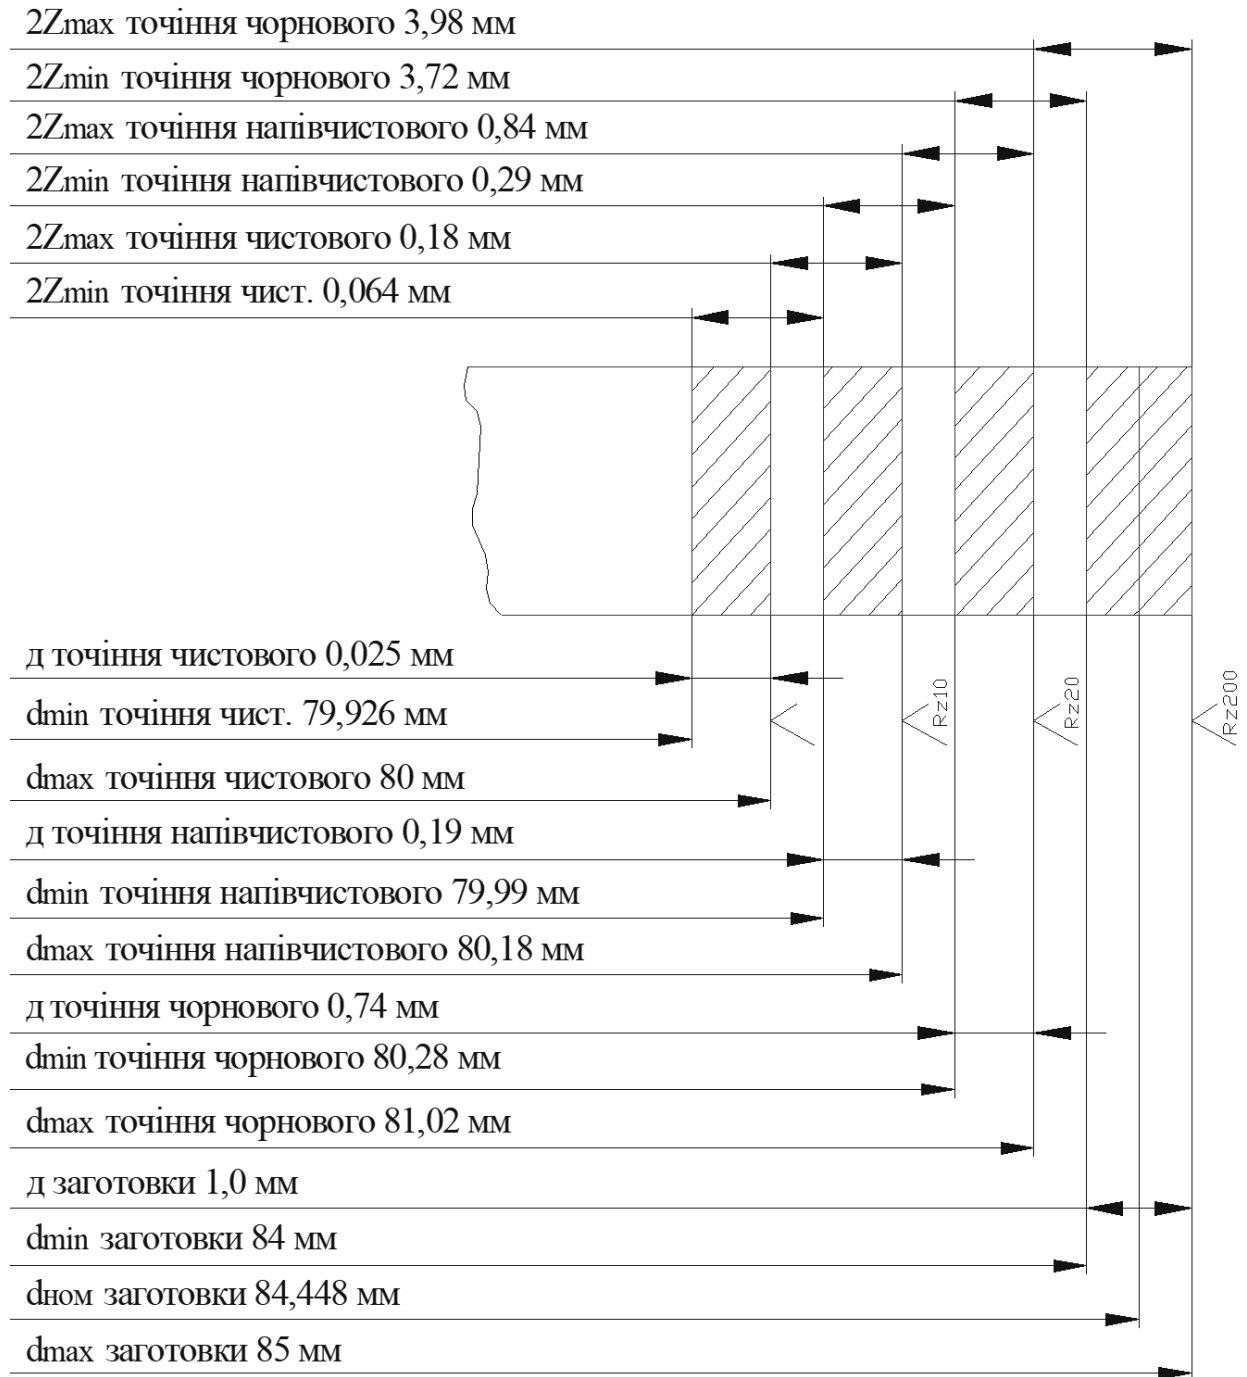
Схема графічного розташування припусків та допусків для поверхні $\varnothing 80h9$
